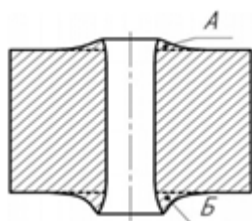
Схема наплывов металла на торцах заготовок, обработанных дорнованием:
